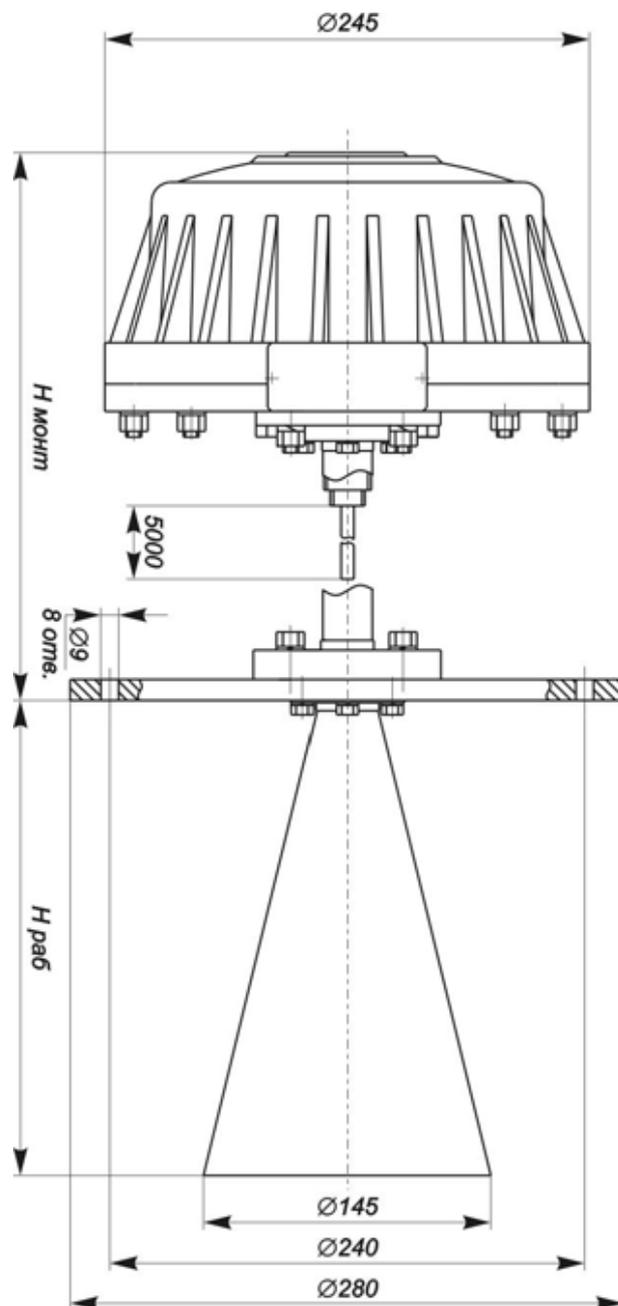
Габаритные и установочные размеры БАРС351И
